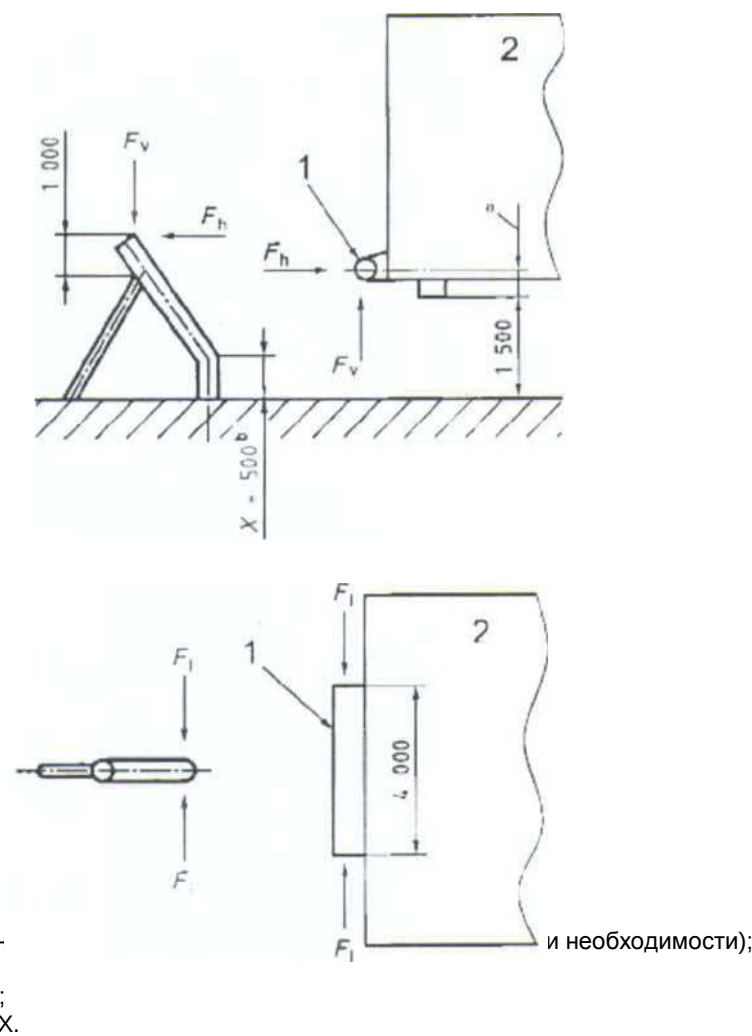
Вертикальный рогообразный тип направляющего устройства с горизонтальным амортизатором
